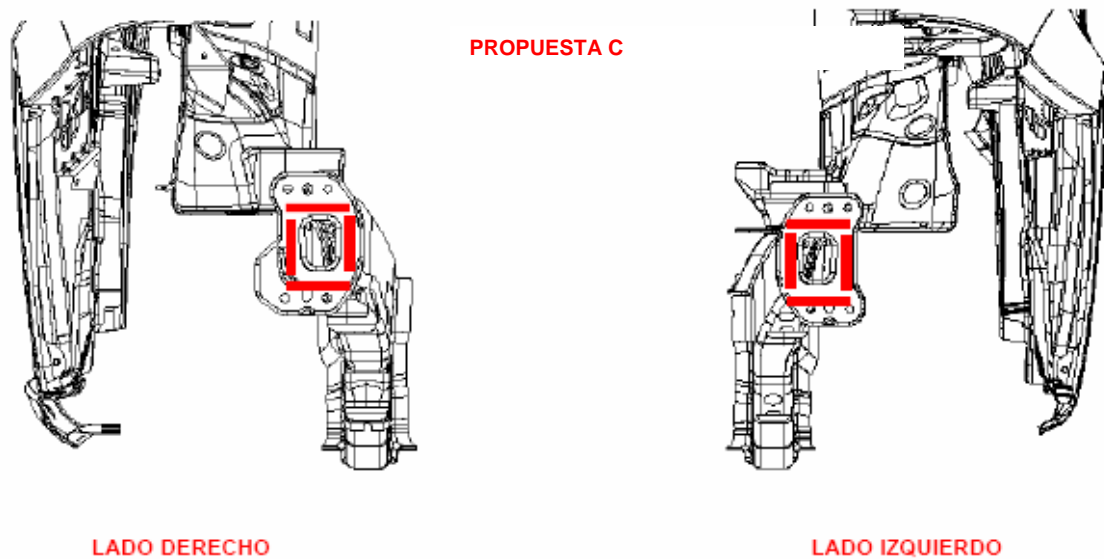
Implementación de la Propuesta C para la soldadura automática
